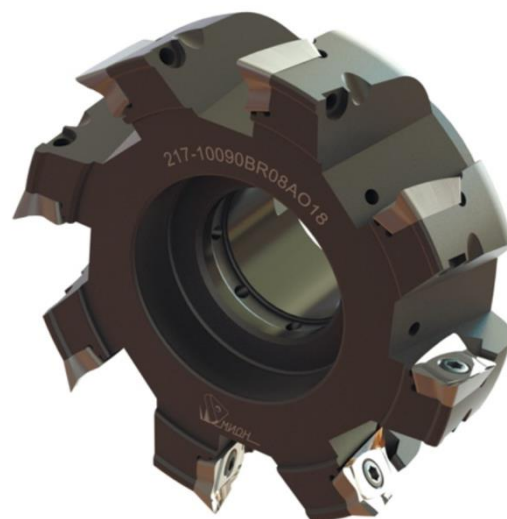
Торцевая насадная фреза №217 с СМП для обработки алюминия и алюминиевых сплавов изготовленной в ООО «ПК МИОН».
